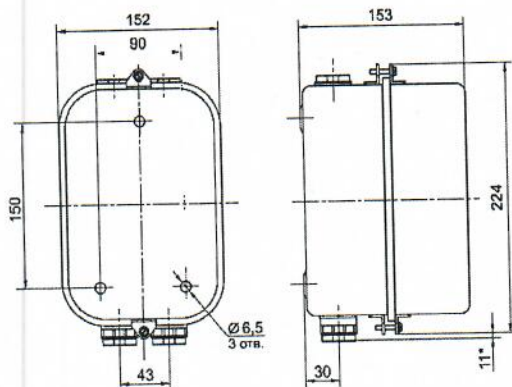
Пускатель ПМ12-040 40А в защитном корпусе. Степень защиты - IP40; IP54
